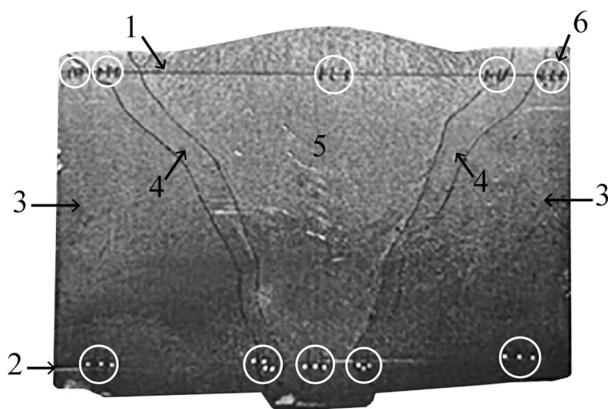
Общий вид металлографического шлифа сварного соединения из стали 10ХСНД после СЭТО с расположением зон сварки, линий и точек замеров микротвердости (образец № 3, температура нагрева 950–980 °С): 1, 2 — линии замеров микротвердости; 3 — основной металл; 4 — зона термического влияния; 5 — сварной шов; 6 — точки замеров микротвердости
